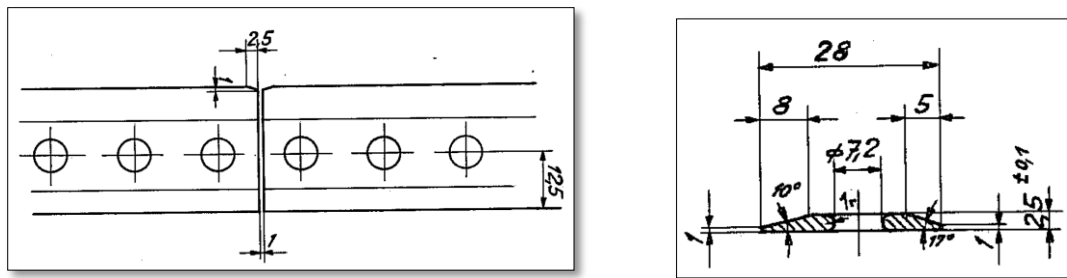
dimensioni del bendaggio del 6° stadio della macchina n° 2.
